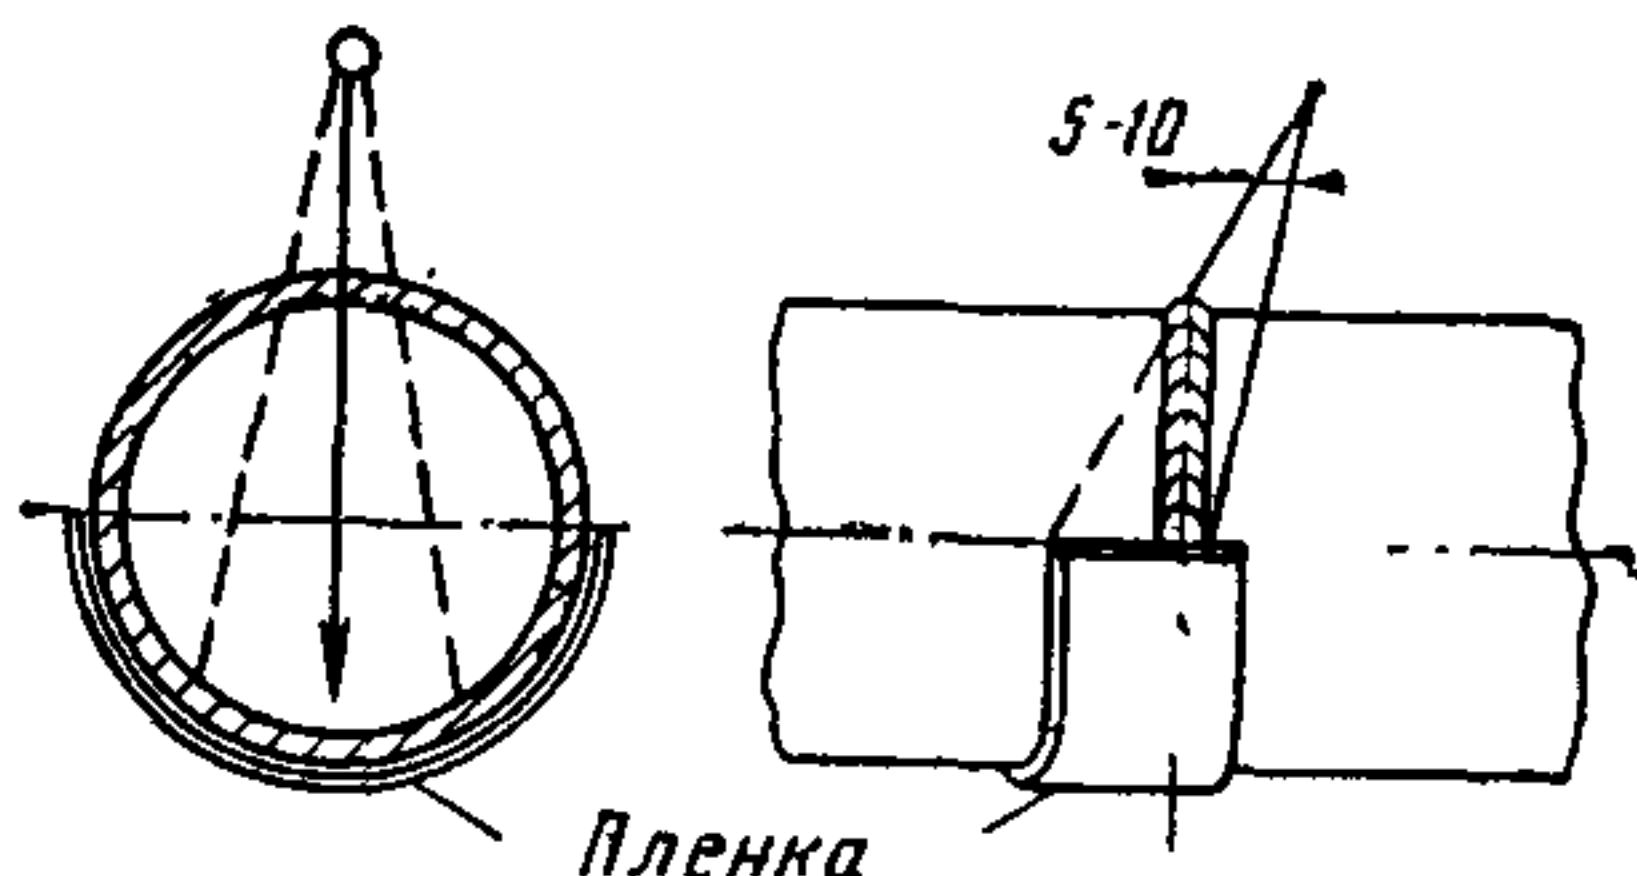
Просвечивание сварных стыков труб малого диаметра через две стенки за одну установку источника излучения
